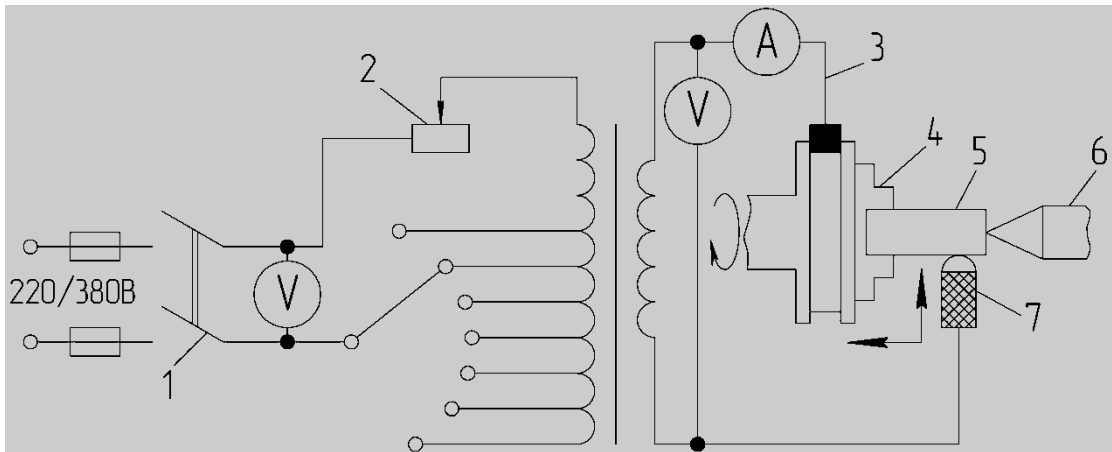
Принципиальная схема электромеханической обработки детали на токарном станке (1- рубильник; 2 - реостат; 3 - вторичная обмотка; 4 - патрон; 5 - деталь; 6 - задняя бабка; 7 — инструмент)
